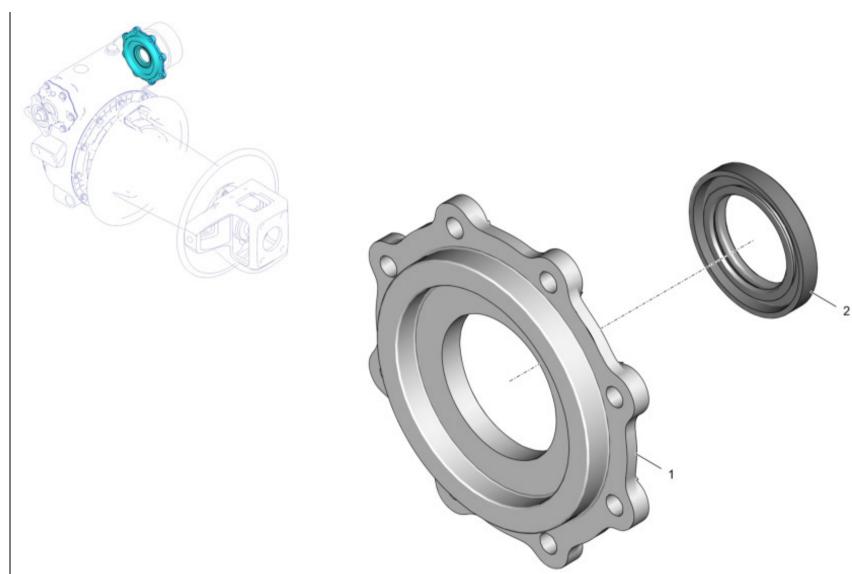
375-4501050-В Крышка упорного подшипника червяка лебедки
